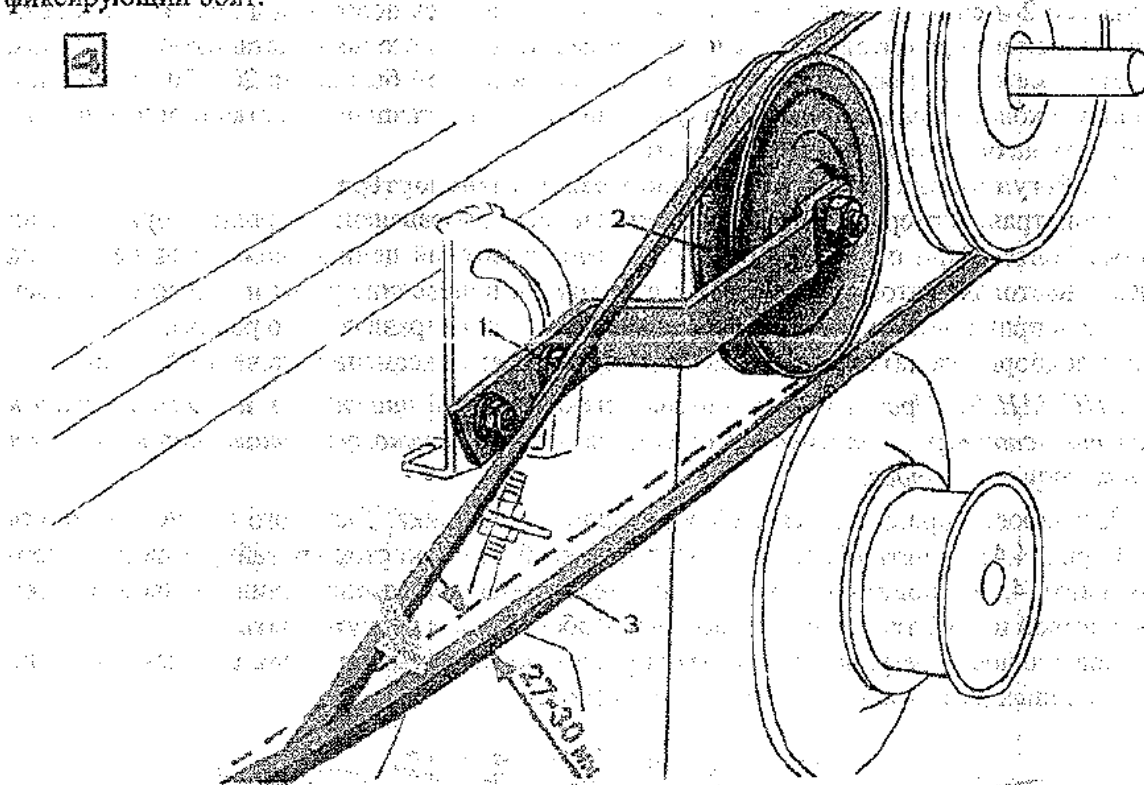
Схема регулировки натяжения приводного ремня: 1 - болт фиксирующий; 2 - натяжной ролик; 3 - ремень
